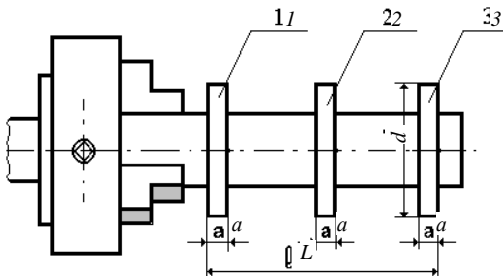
Схема для проверки обеспечения токарным станком точности геометрической формы: 1, 2, 3 – пояски;  $a$  – ширина пояска;  $d$  – диаметр пояска
